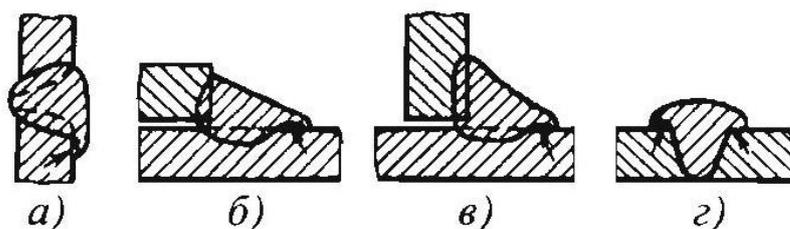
Наплывы в швах: а – горизонтальном; б – нахлесточного соединения; в – таврового соединения; г – стыкового соединения или при наплавке валиков
